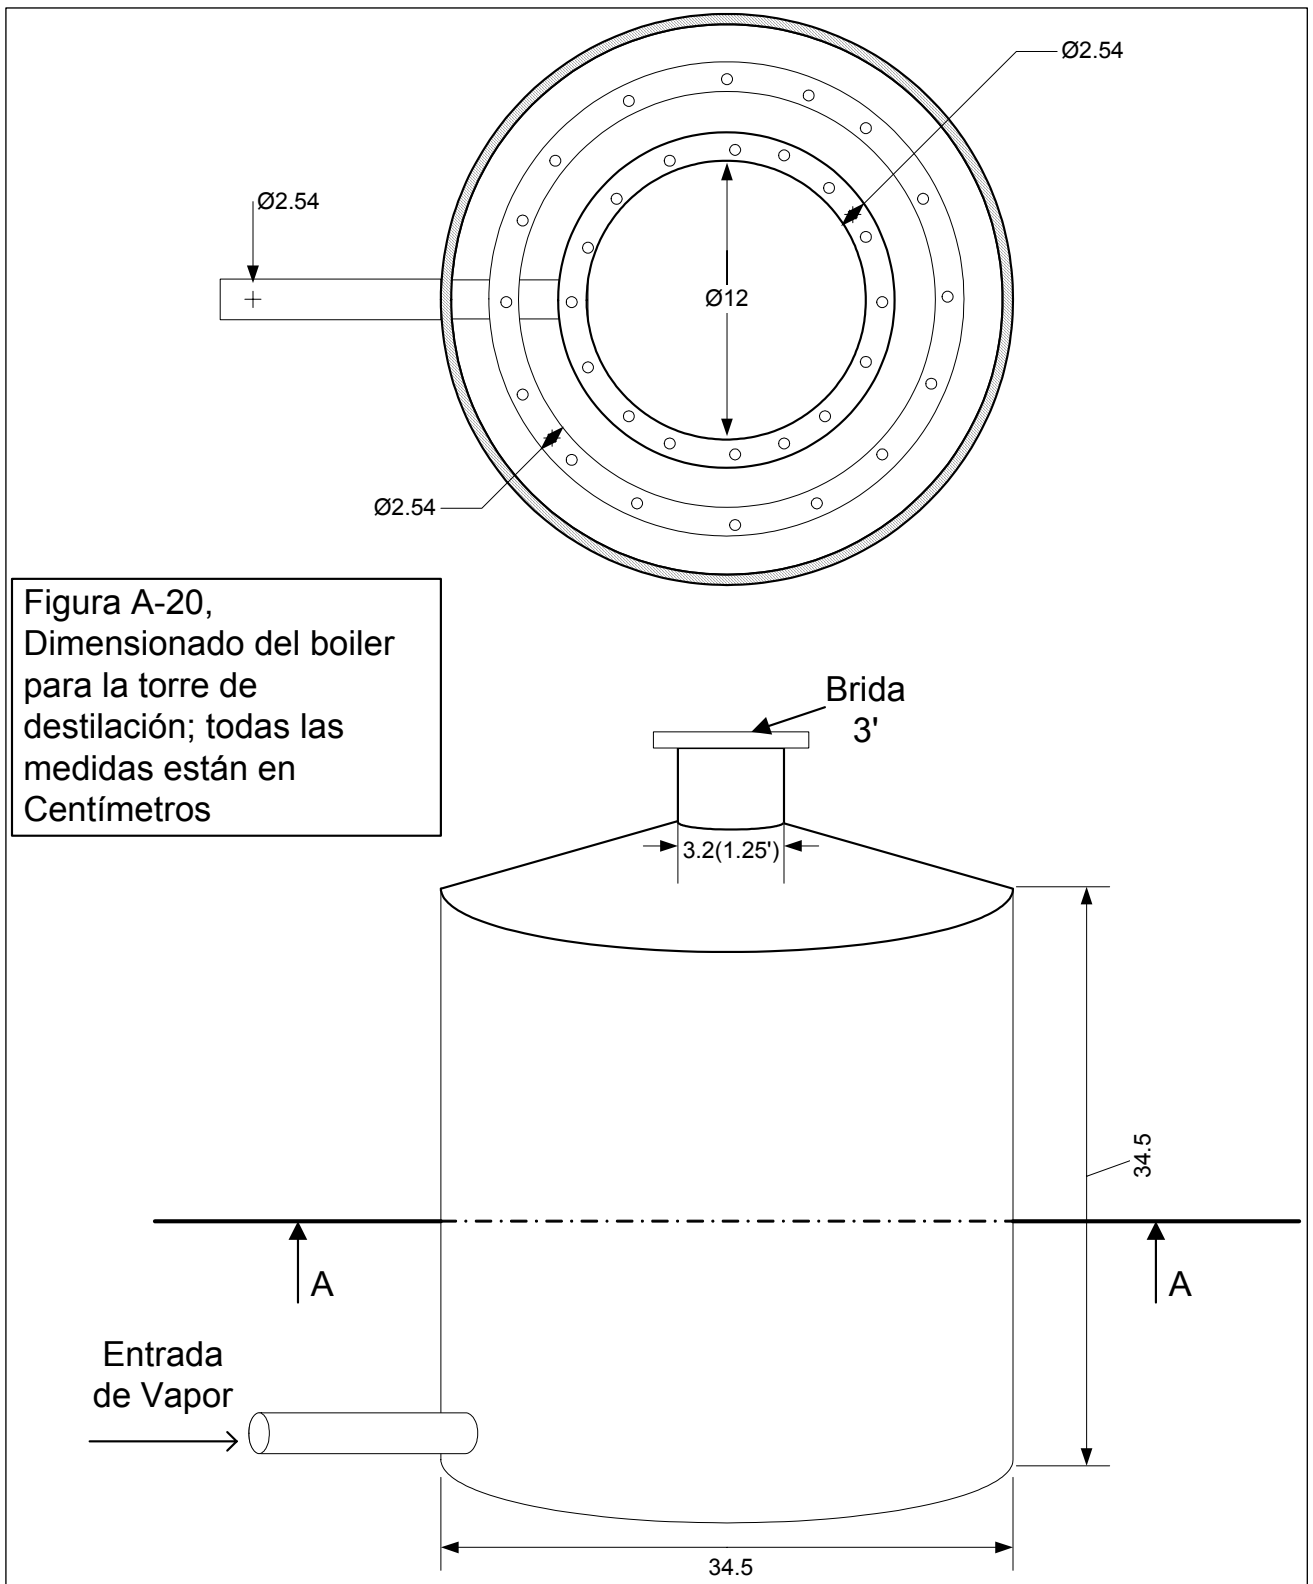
Dibujo y Dimensionado de Boiler para equipo diseñado a nivel piloto
